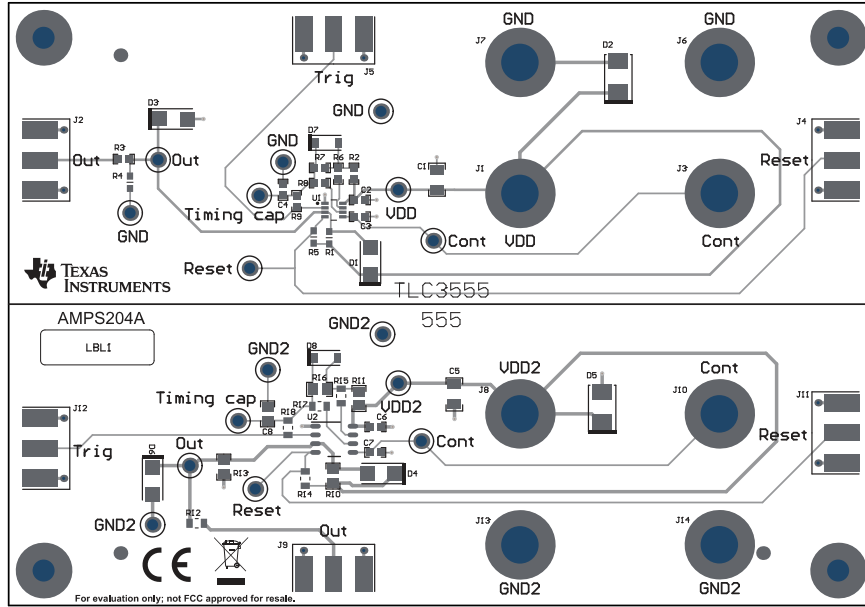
TLC3555EVM PCB 布局顶部复合视图
